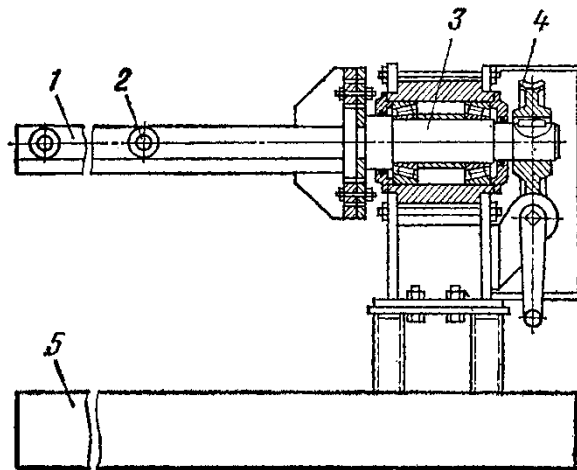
Стенд для розбирання двигунів вилочної конструкції
